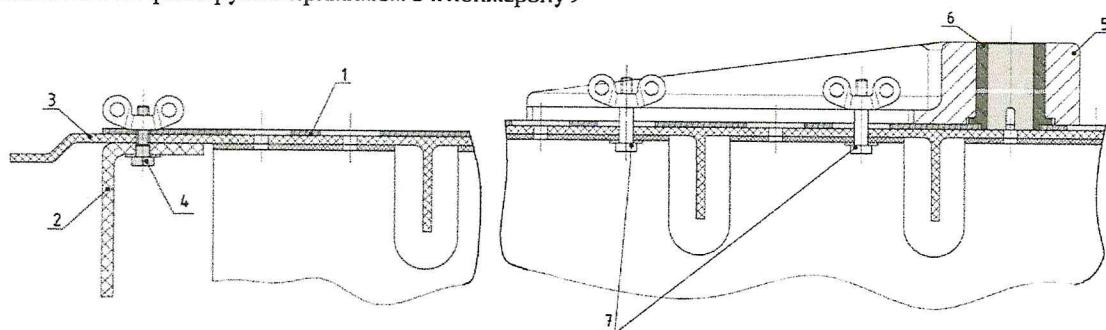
Поперечное сечение кондуктора для сверления отверстий по нервюрам
